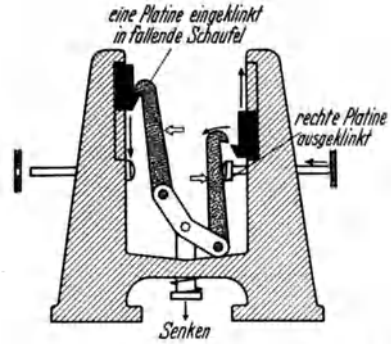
Linke Schaufel mit linker Platine oben. Kein Loch in der rechten Karte. Schaft wird sinken.
